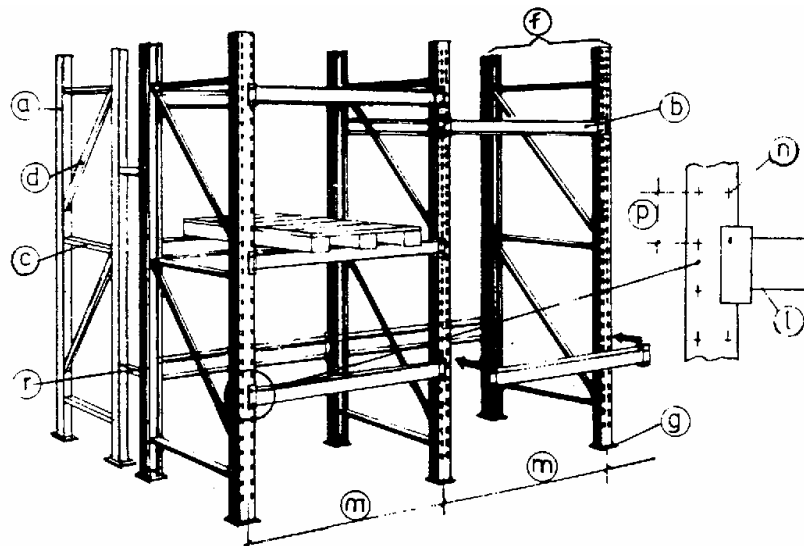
Estructura para palets*: a. Montante, b. Larguero, c. Travesaño, d. diagonal, f. escalera, g. pie, l. fijación, m. cuerpo, n. alojamiento fijación p. paso, r. ensamble. (fuente normas UNE: 58-003-78)
